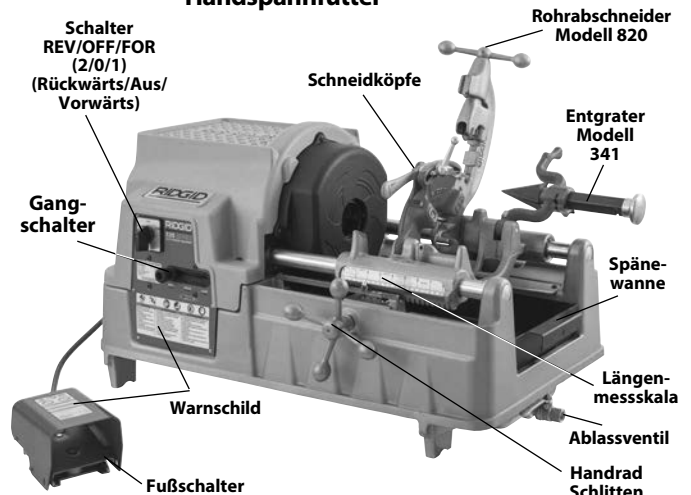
A – Gewindeschneidmaschine 535 mit automatischem Spannfutter
